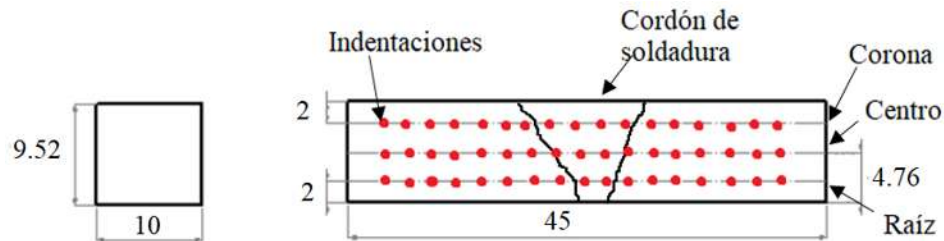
Probetas de uniones soldadas para ensayo de microdureza Vickers (cotas en mm).
